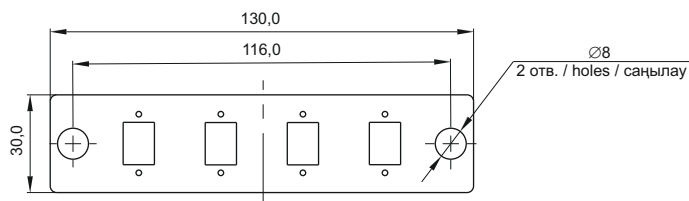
Габаритные и установочные размеры панели FOBX-P04-SC-R / Figure 4 – Overall and mounting dimensions of the panel FOBX-P04-SC-R / 4 сурет – FOBX-P04-SC-R панелінің габариттік және орнату өлшемдері
